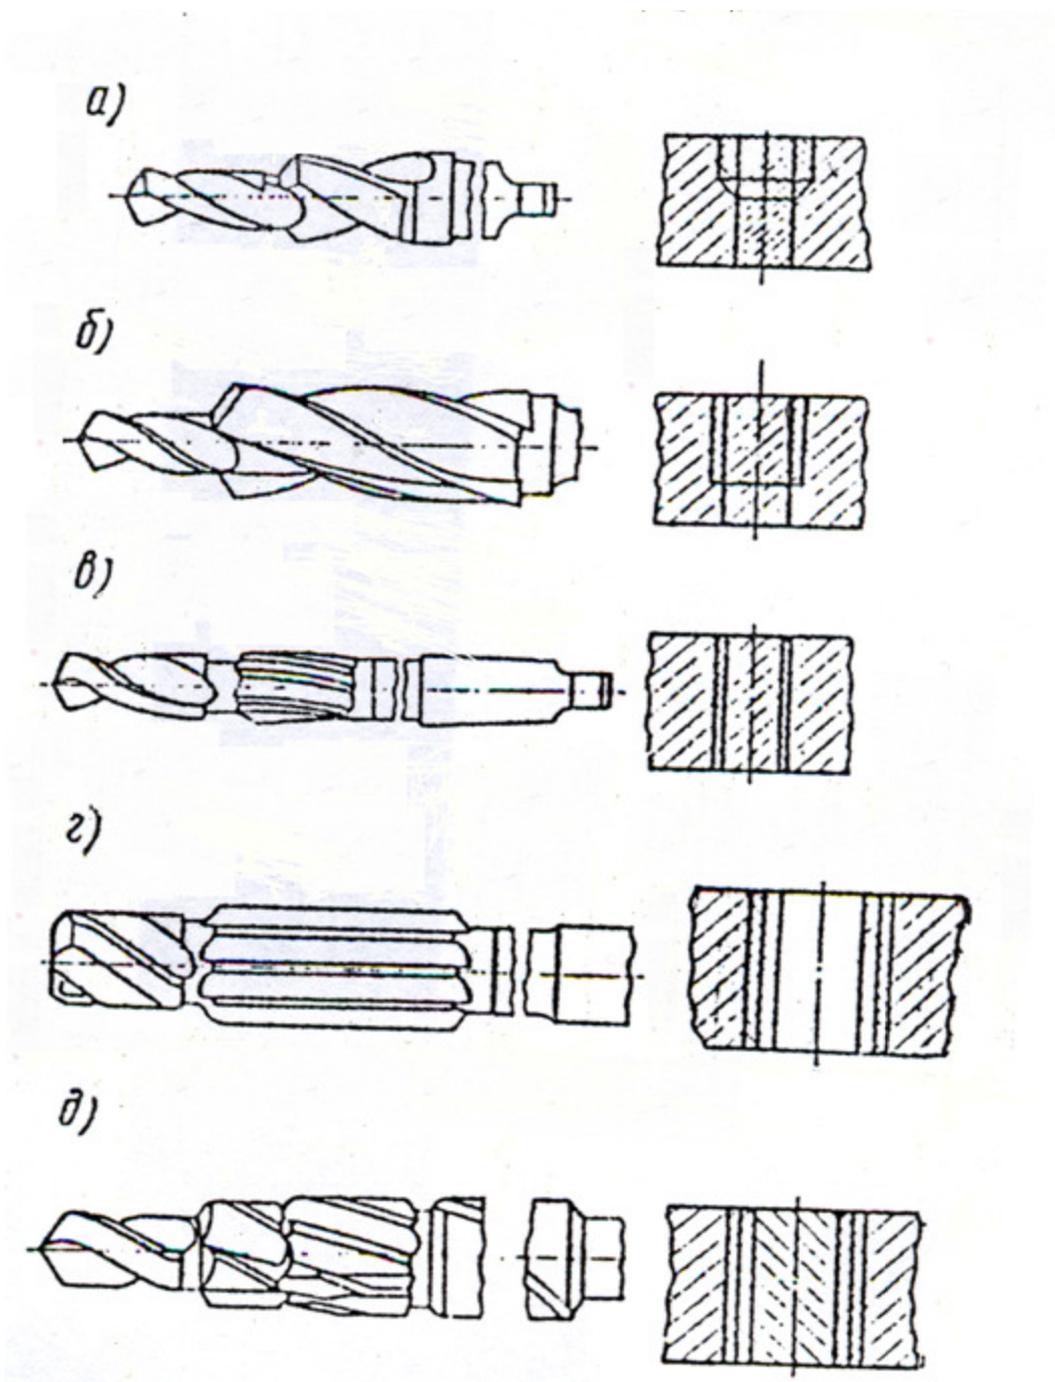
Комбинированные режущие инструменты: а) сверло-сверло, б) сверло-зенкер, в) сверло-развертка, г) зенкер-развертка, д) сверло-зенкер-развертка
